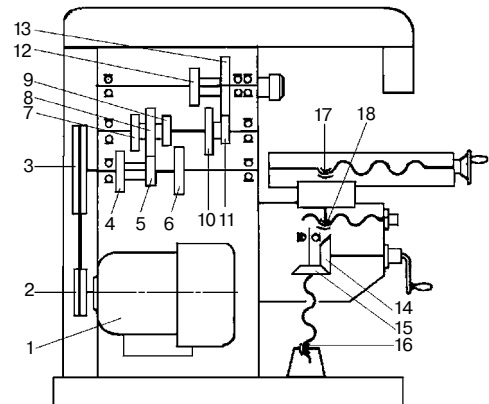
Кинематическая схема фрезерного станка НГФ-110Ш4: 1 — электродвигатель; 2 — шкив электродвигателя Ø86 мм; 3 — шкив коробки скоростей Ø136 мм; 4, 5 — зубчатые колеса с числом зубьев 34 и 25; 6 — зубчатое колесо с 43 зубьями; 7, 8, 9 — зубчатые колеса переднего блока с числом зубьев 50, 59, 41; 10, 11 — подвижный блок с числом зубьев 57 и 25; 12, 13 — неподвижные зубчатые колеса с числом зубьев 43 и 75; 14, 15 — конические зубчатые колеса; 16 — винт вертикального перемещения стола; 17 — винт поперечной подачи; 18 — винт продольной подачи
